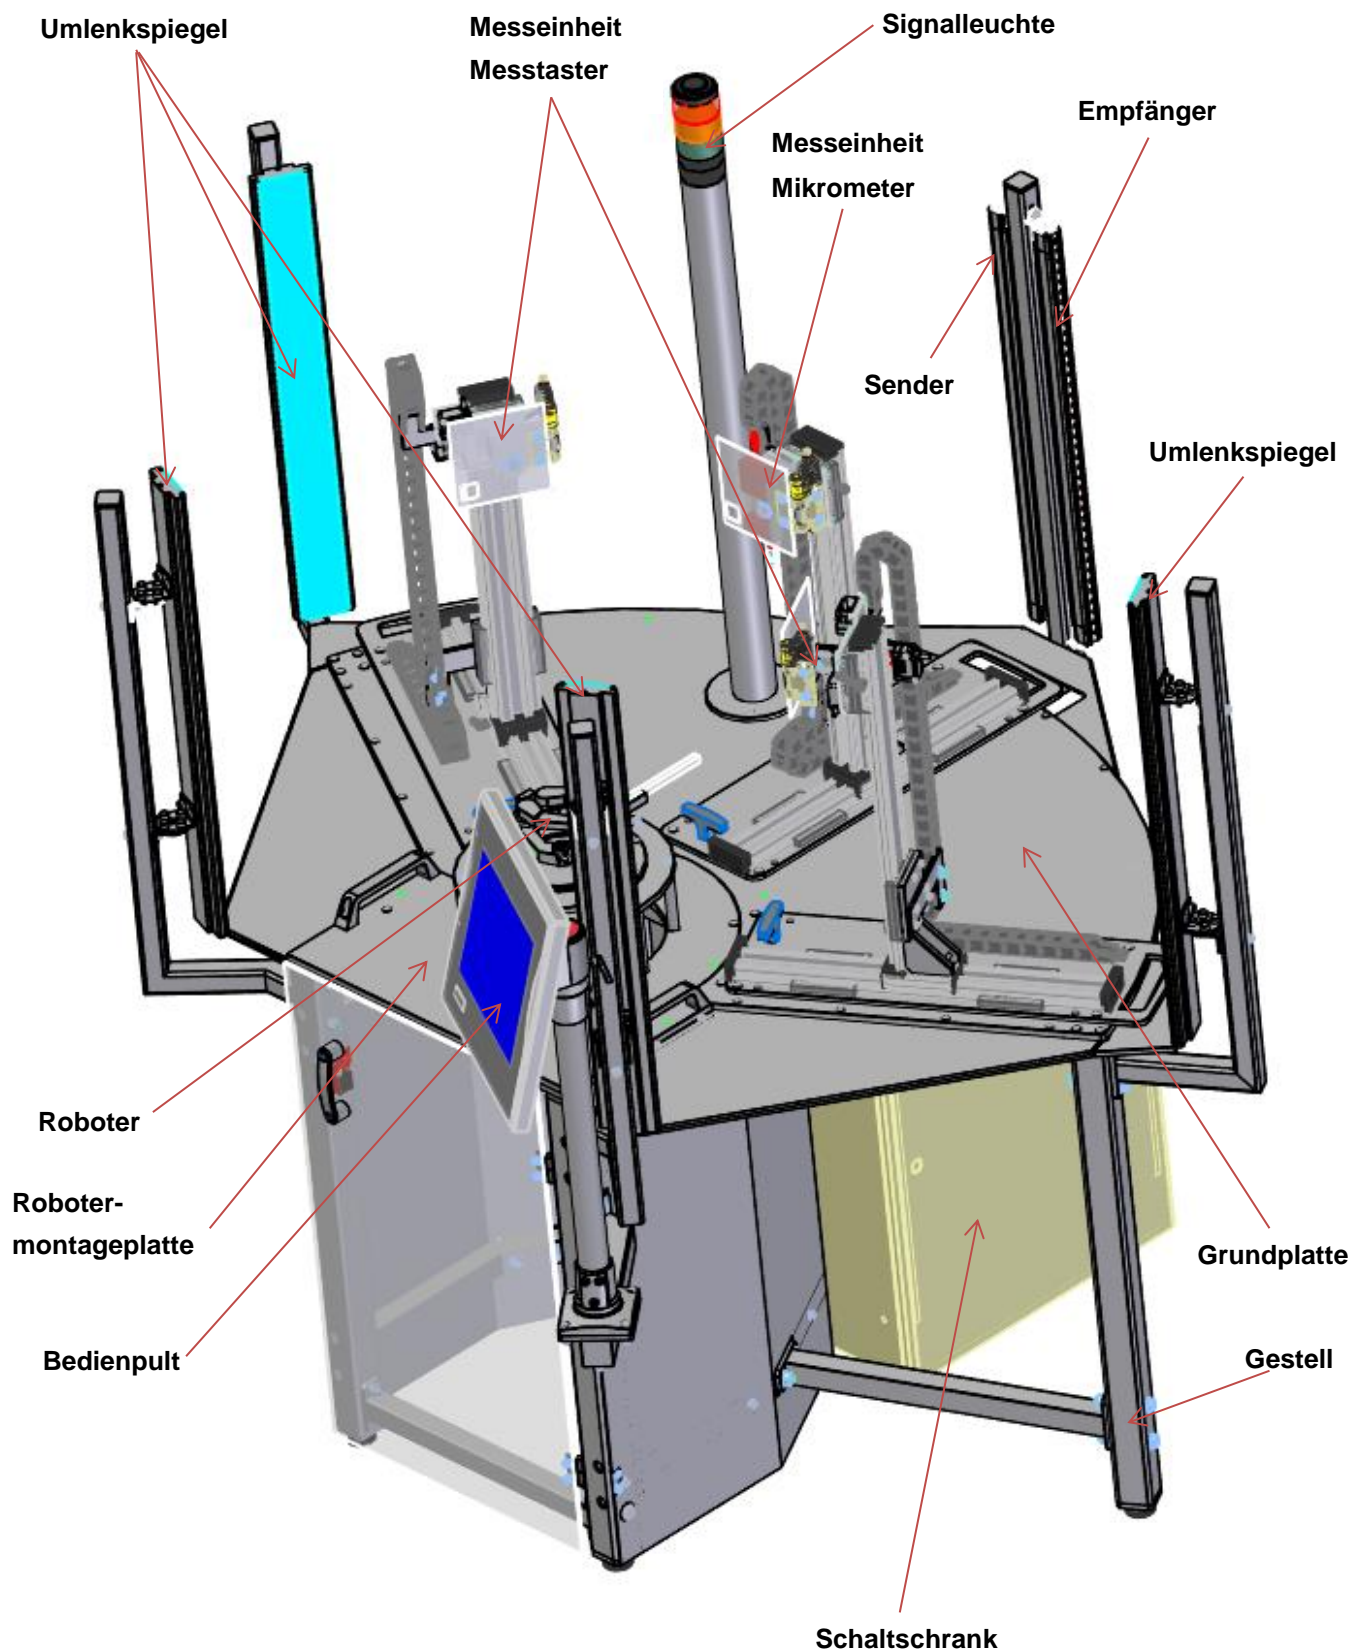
Roboterprüfstand mit einem P-5000 Roboter
